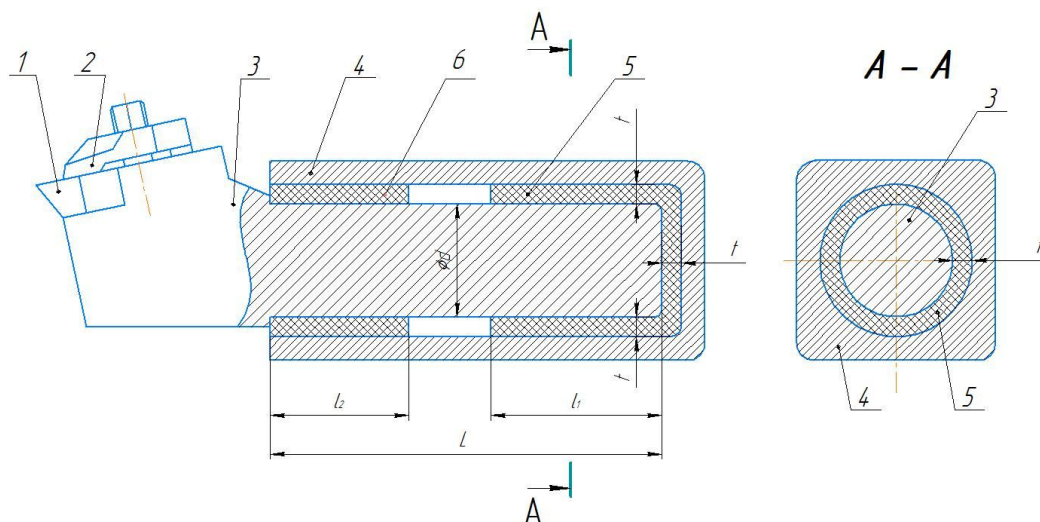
Резец с демпфирующими полувставками различной жесткости: 1 – режущая пластина; 2 – узел крепления пластины; 3 – державка; 4 – стакан; 5, 6 – полувставки демпфирующие
